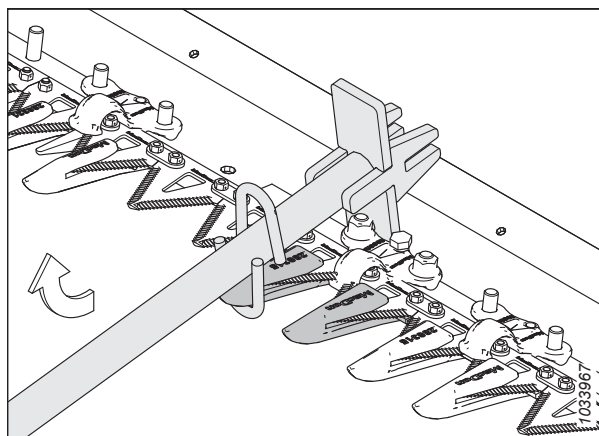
Регулировка смещением вверх — заостренный противорежущий палец
